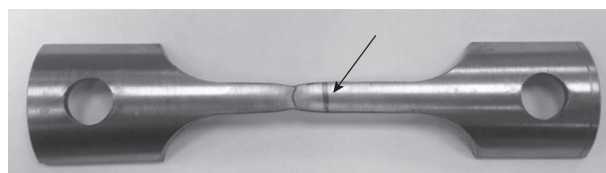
Образец сварного соединения после испытаний на статическое растяжение (стрелкой помечен сварной стык).
